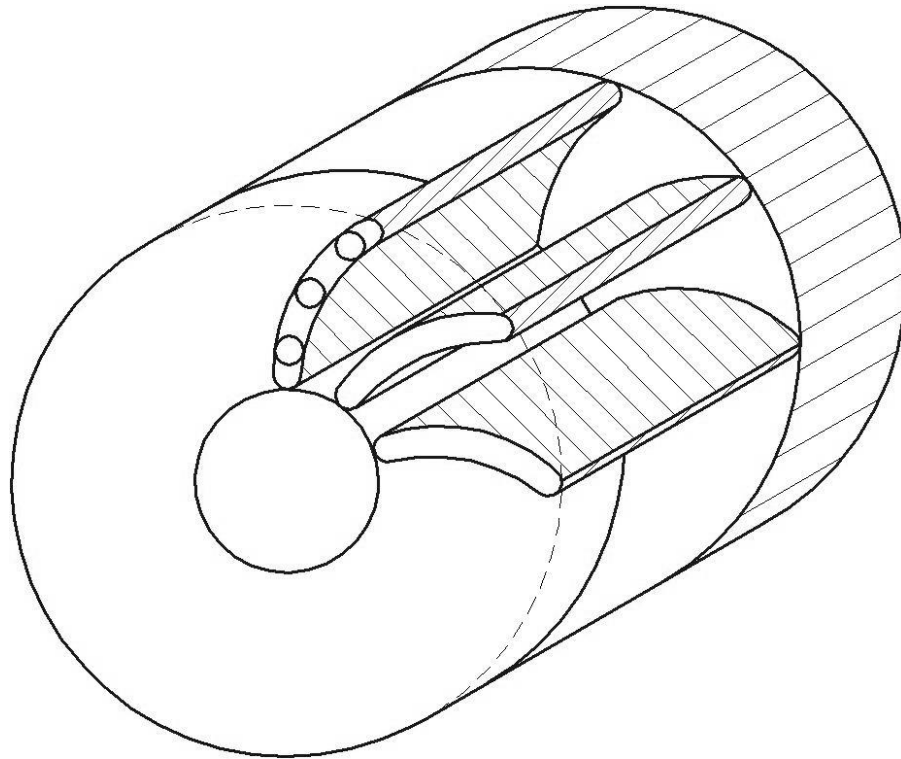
Схема рабочего диска колеса центробежного компрессора.
